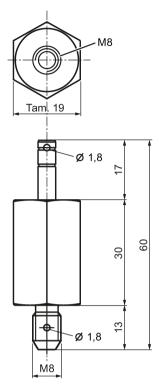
Desenho de dimensões do suporte de substituição rápida 6GT2690-0AH00
